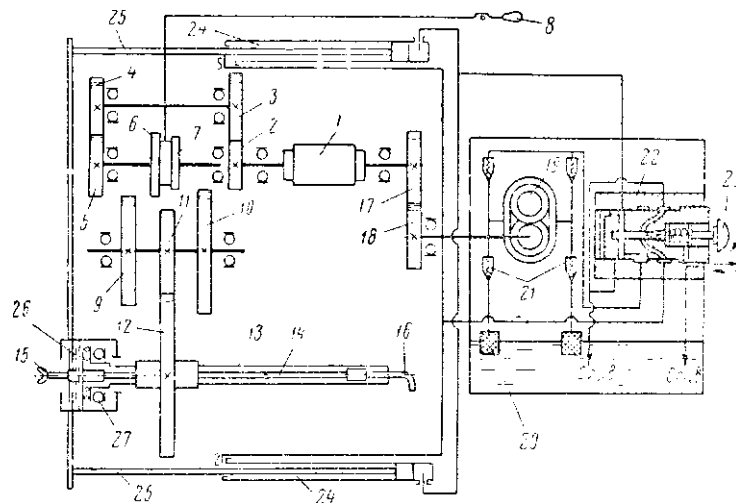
Схема устройства колонкового электросверла с гидравлической подачей
